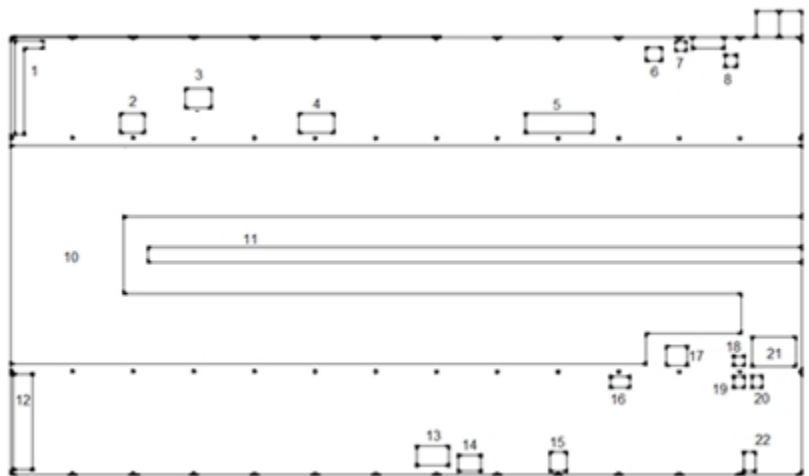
Distribución de áreas de trabajo y maquinaria en planta baja
